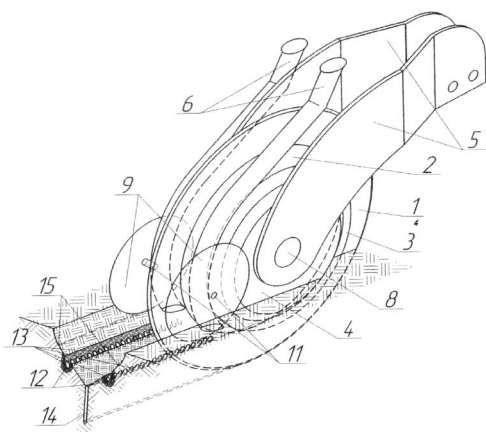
Технологическая схема работы комбинированного однодискового сошника с двухсторонними ребрами и дисковыми загорточами: 1 – плоский диск; 2 – внутренняя ребра; 3 – бороздкообразователь; 4 – наружная ребра; 5 – корпус; 6 – семянаправители; 8, 11 – оси; 9 – сферические диски; 12 – ложа; 13 – семена; 14 – щель; 15 – бороздки
